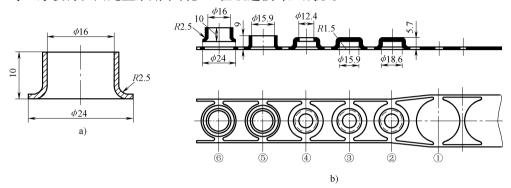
通孔凸缘 a) 零件图 b) 排样图
